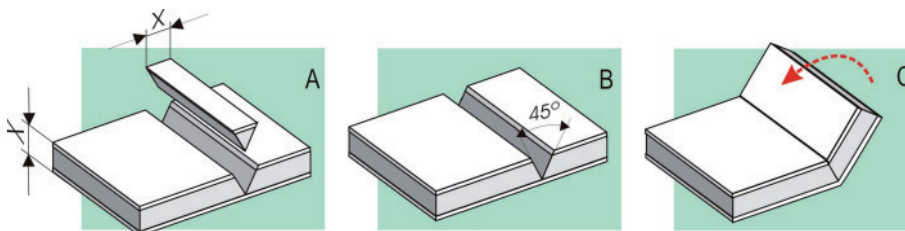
Método para realizar una esquina en ángulo interior de 135° .
